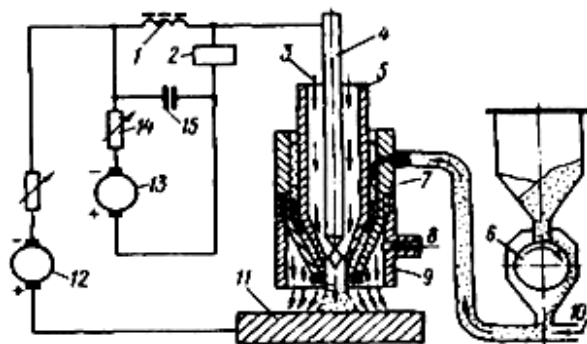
Схема установки для плазменной наплавки с вдвуханием порошка в дугу:
